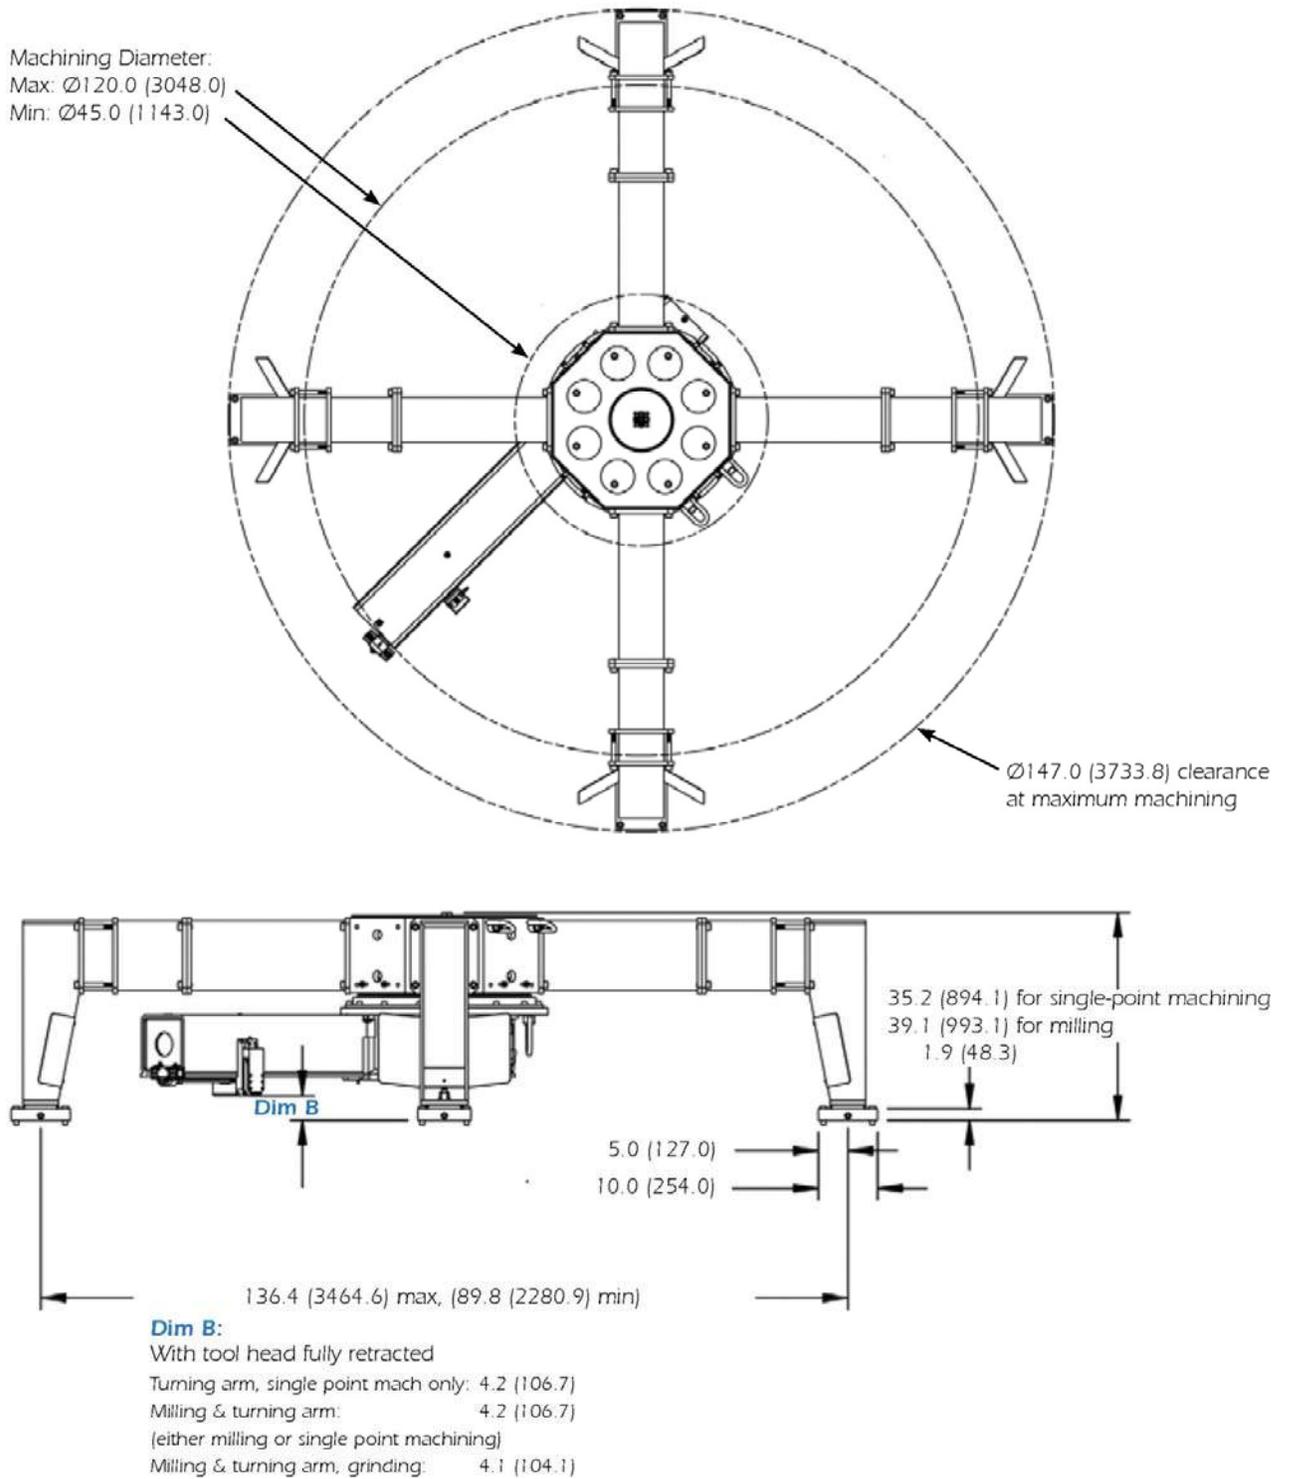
DIMENSIONS DU MANDRIN POUR DE
